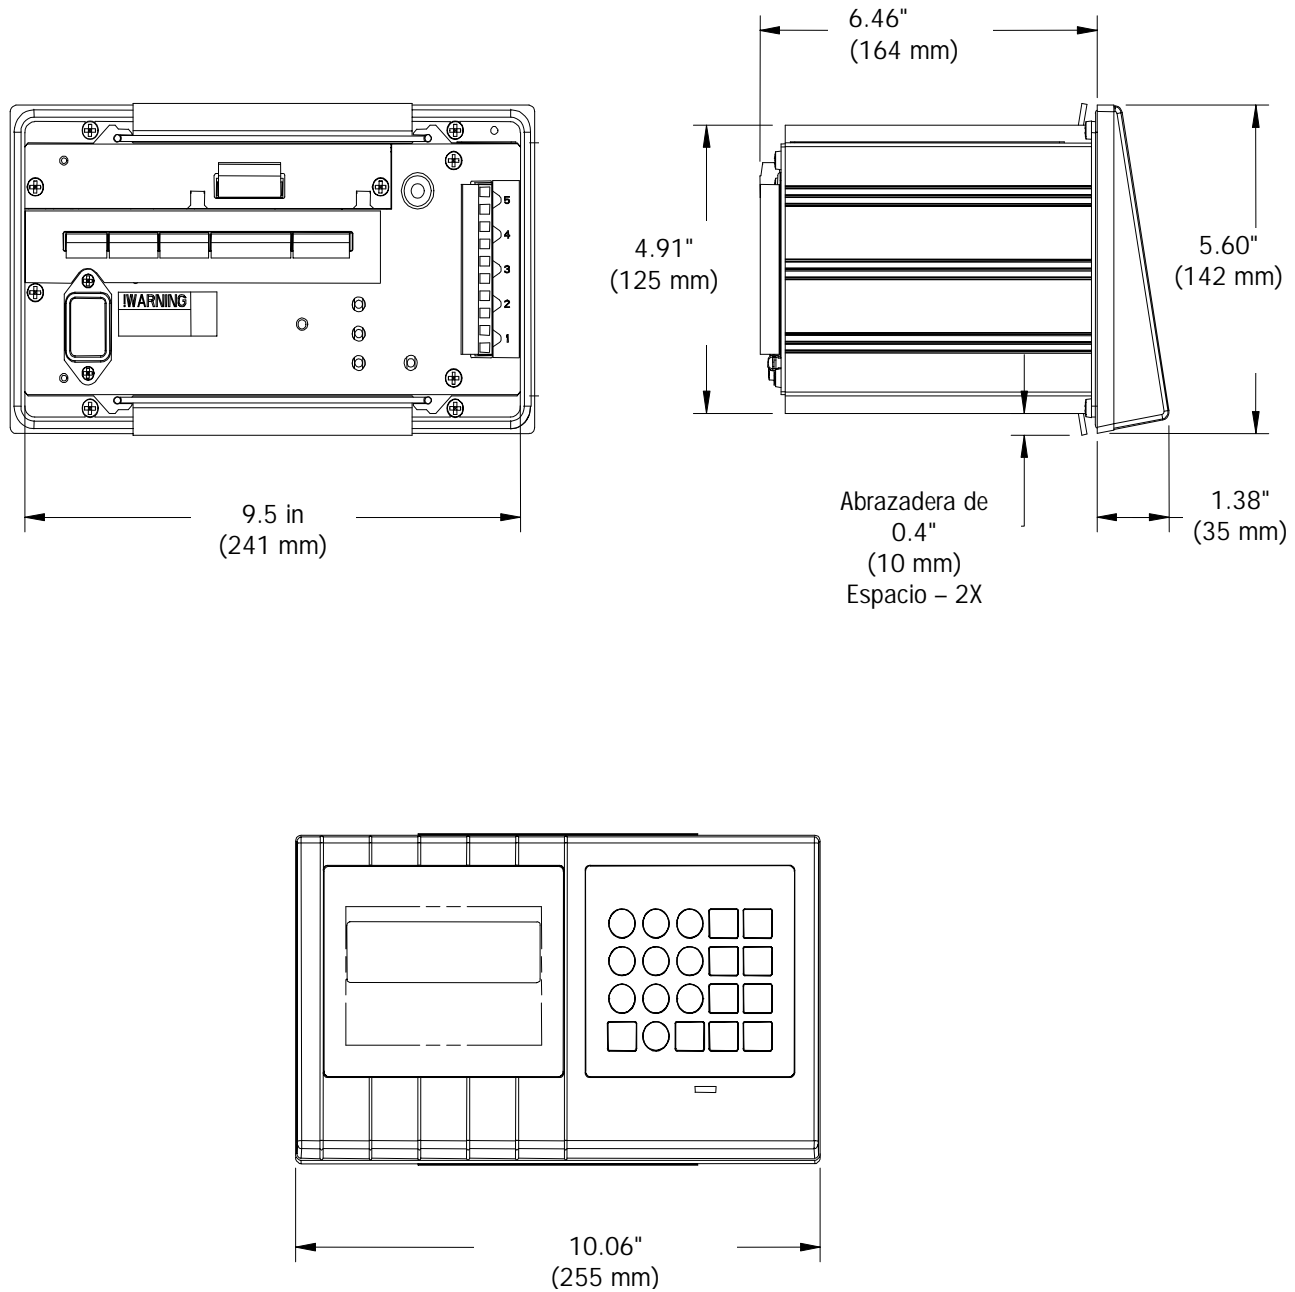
Dimensiones de Montaje de Panel del LYNX
